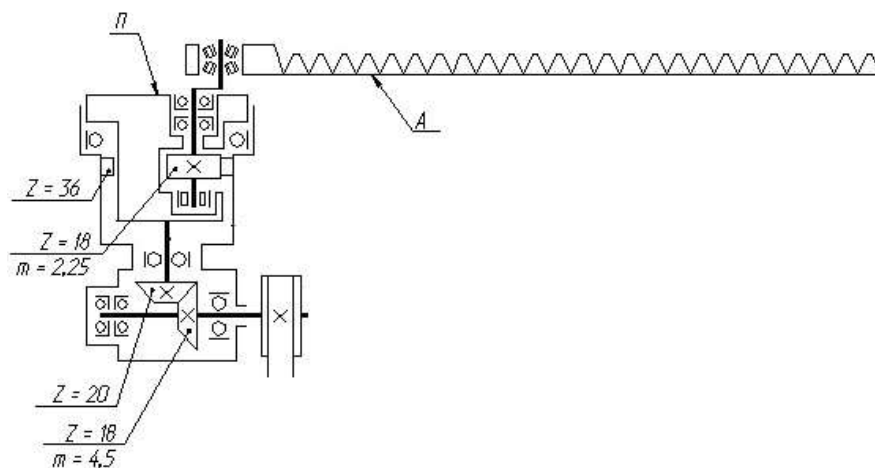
Кинематическая схема привода режущего аппарата жатки: П – планетарный механизм; А – нож режущего аппарата жатки;
